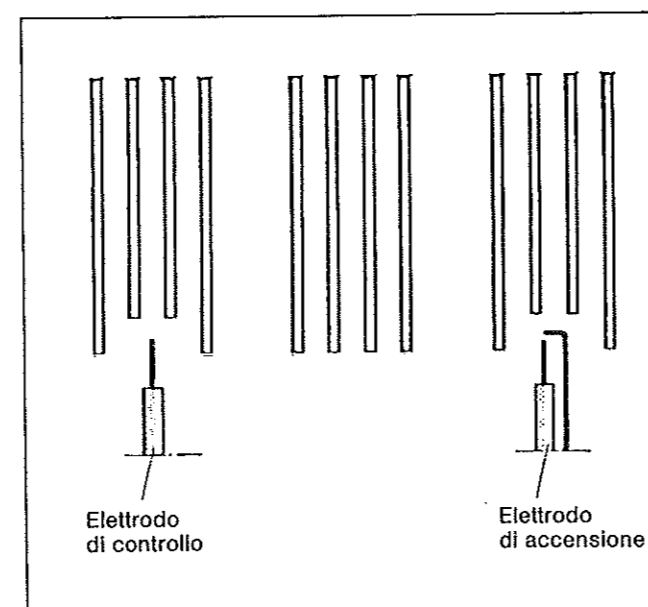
Disposizione delle barrette di raffreddamento vista da sopra.
